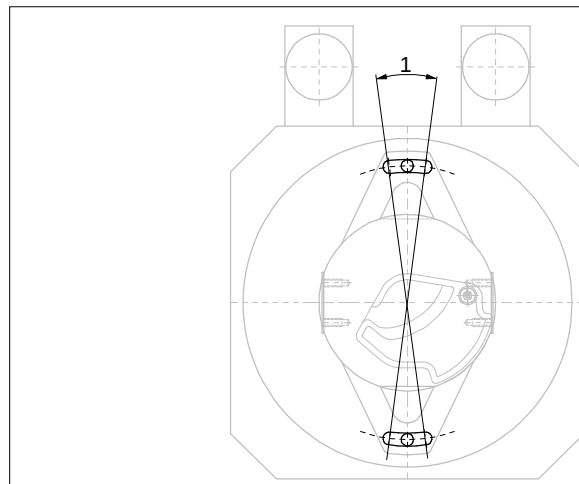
Ausrichtung Geber zu Befestigungsbohrungen
